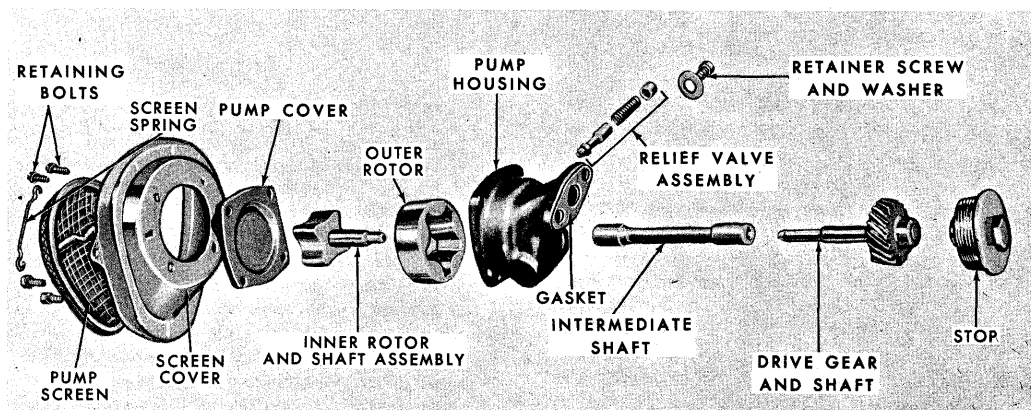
Exploded view af olie pumpen med si, reduktionsventil, aksel og drev.
